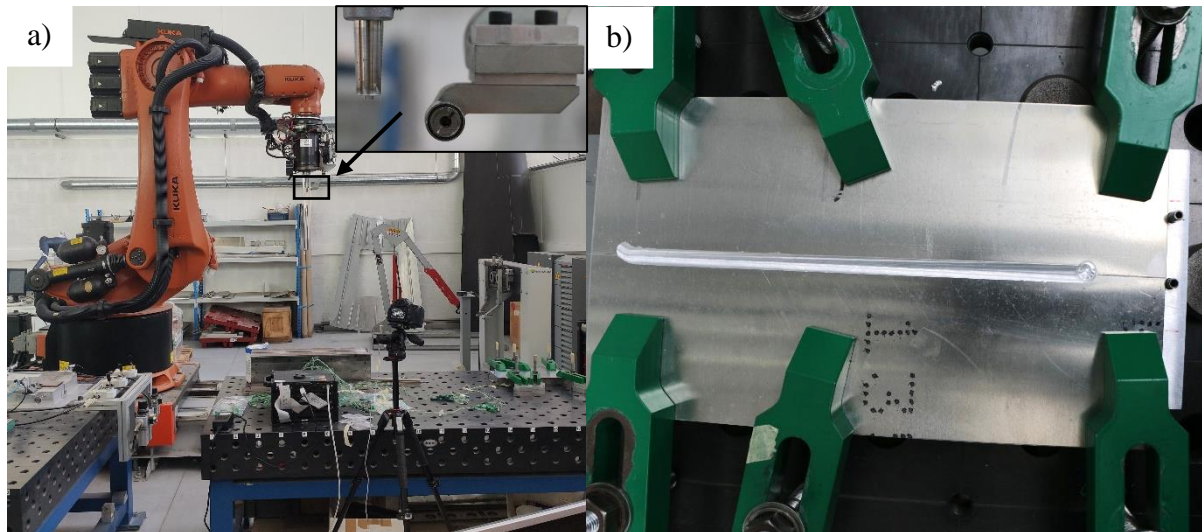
a) robot KUKA KR 500-3MT et son environnement de soudage avec un focus sur l'outil de soudage et sur le rouleau, b) Bridage des tôles sur le support envers (vue après soudage)
